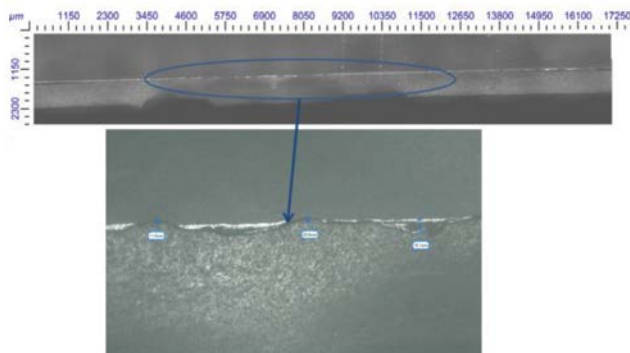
Микроструктура сварного соединения образца № 1 с непроваром по всей площади сварного соединения.
